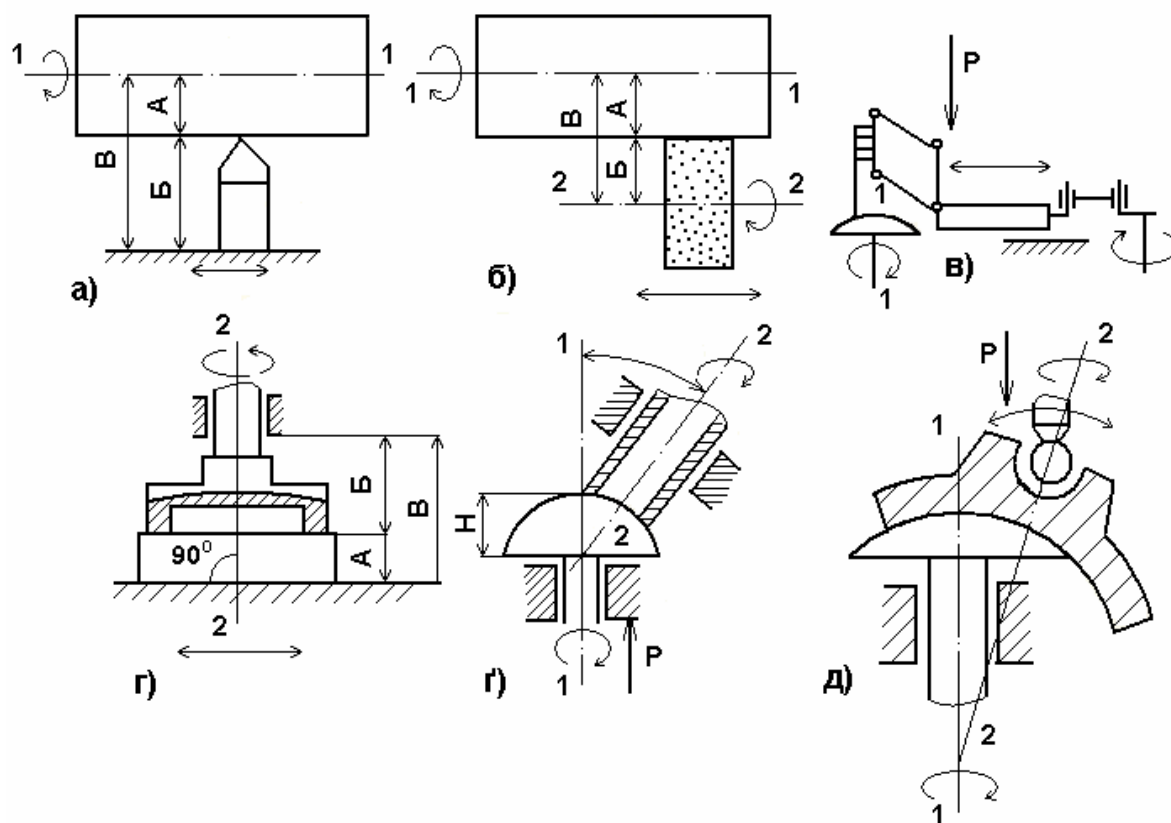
Системи ВПД обробки заготовок оптичних деталей
